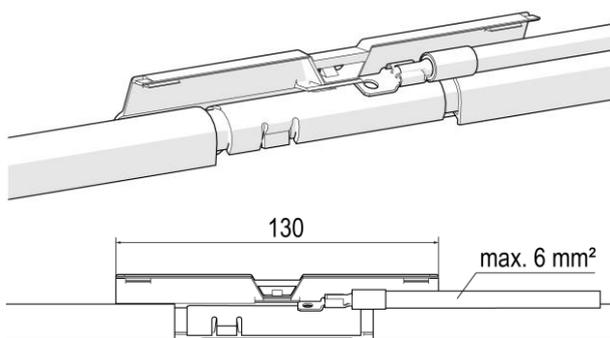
Elektrische Einspeisung mit Verbinder 35 A
